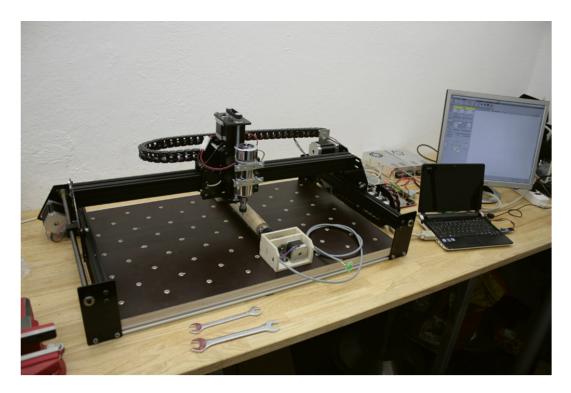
Größeres Kaliber: die Shapeoko-T mit Spindeltrieben, MaXYposi-Steuerung und vierter Achse
